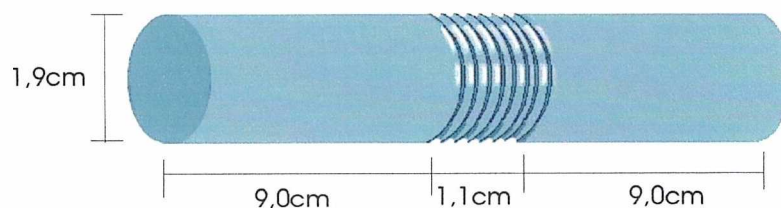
Vista tridimensional e dimensões da haste do fixador
